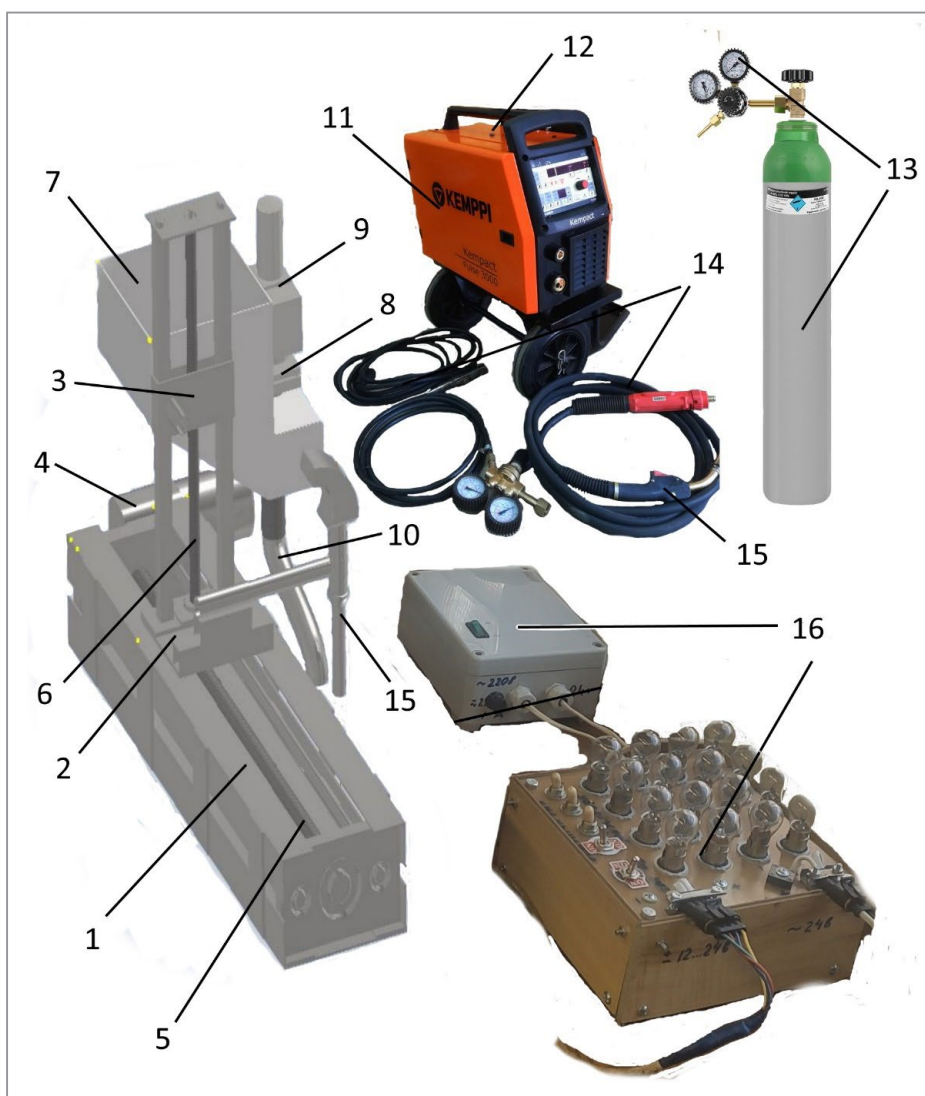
Установка малодеформационной сварки нержавеющей сталей
